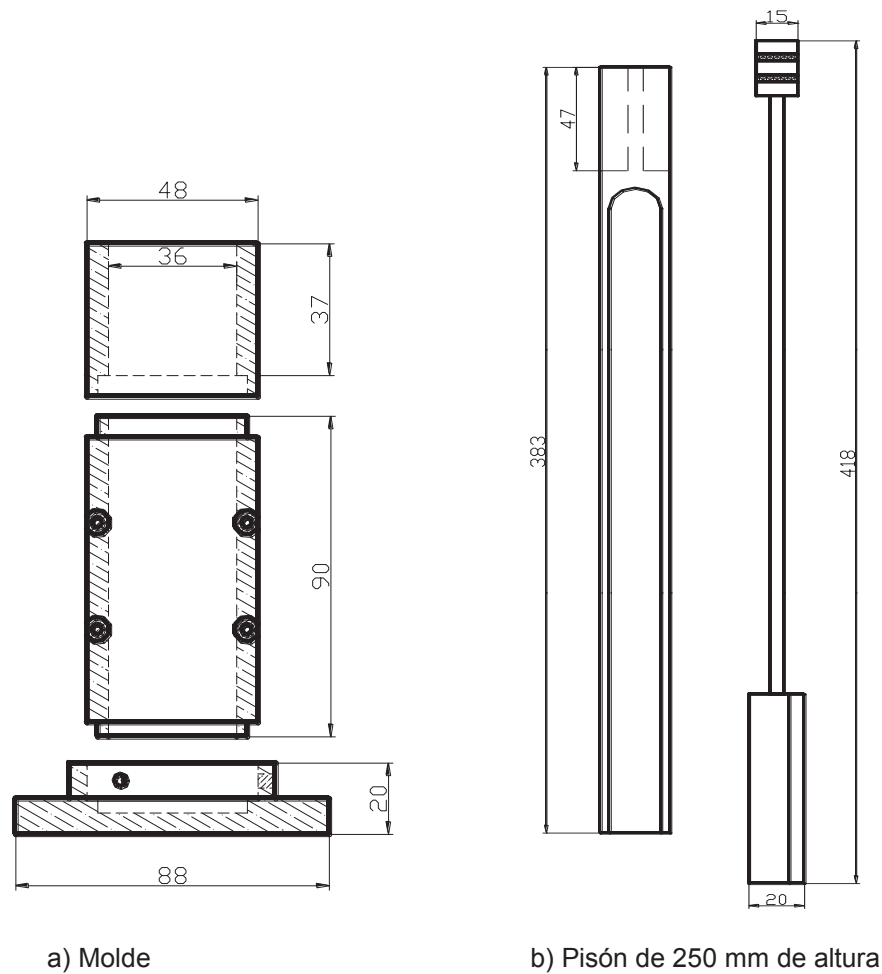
Dimensiones del molde miniatura y del pisón compactador.
